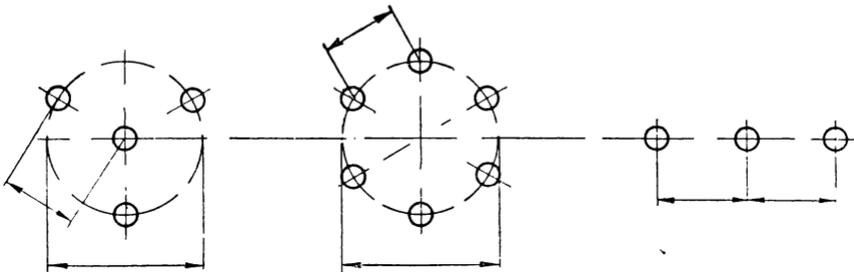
Основные схемы расположения отверстий, обрабатываемых при помощи универсальных сверлильных головок
